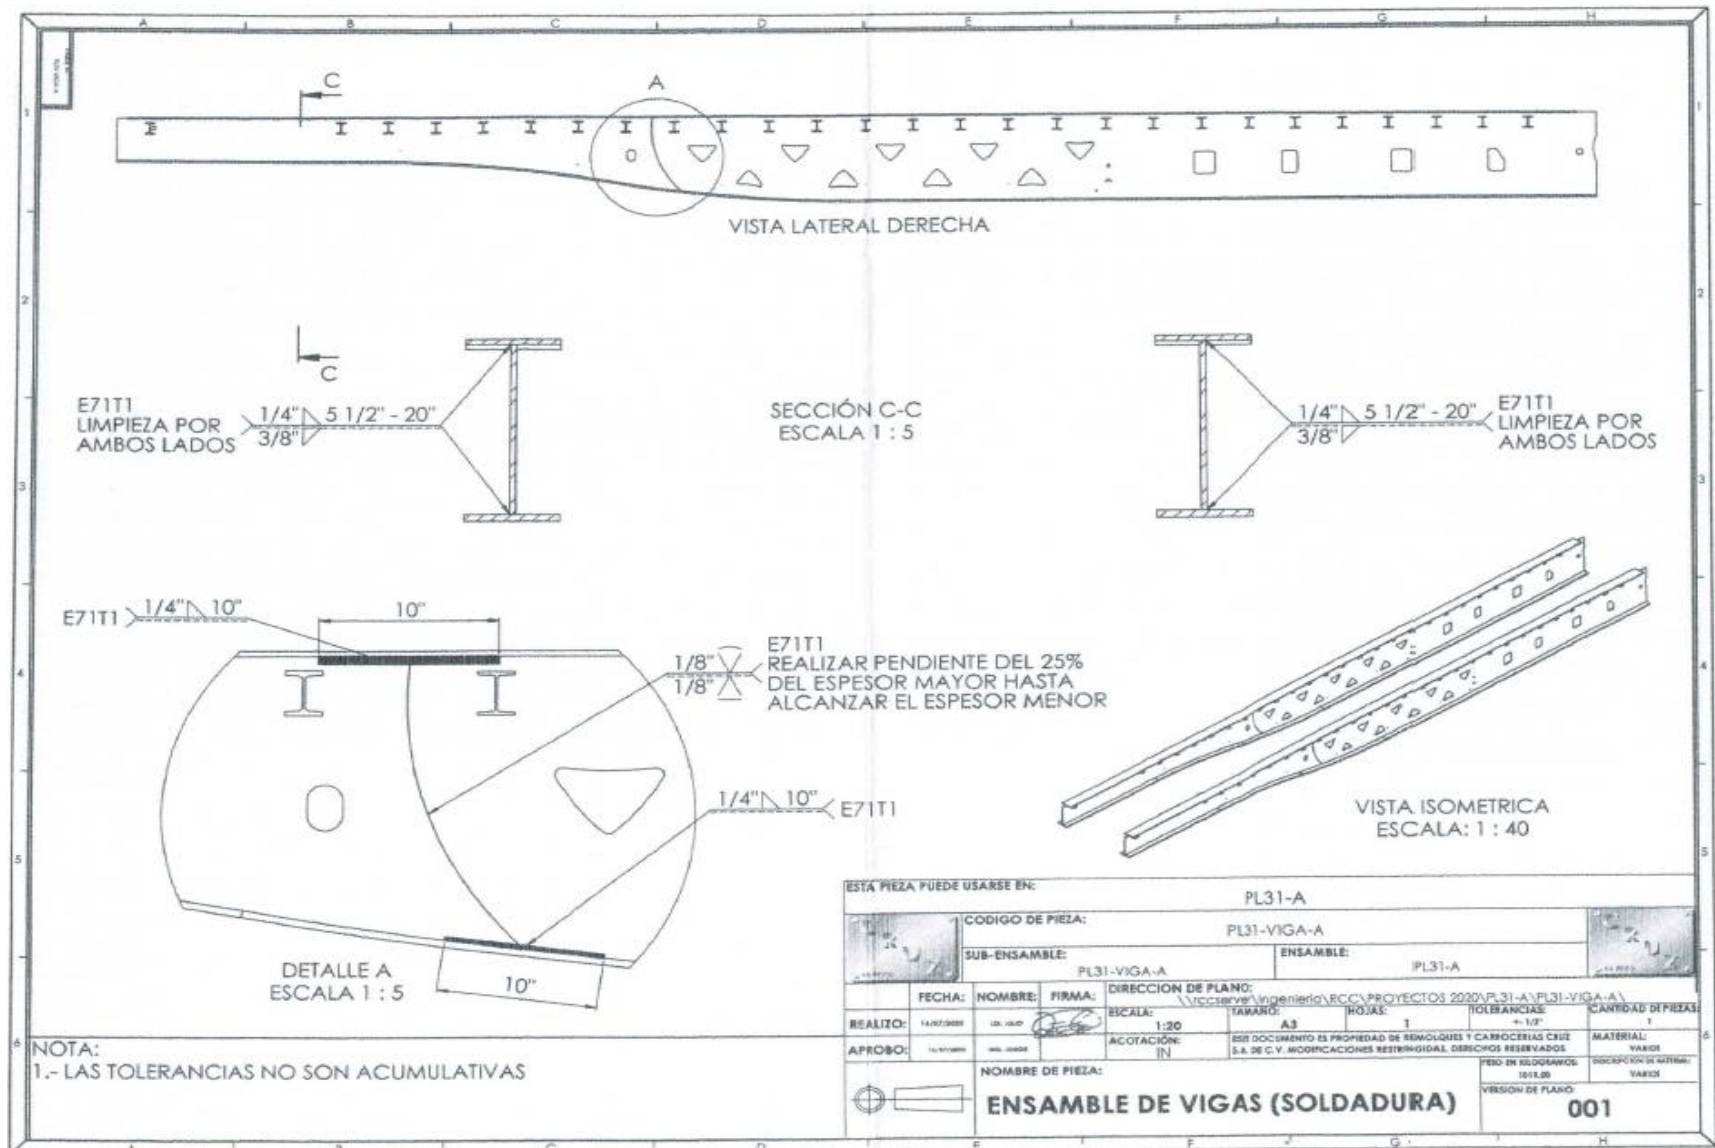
Plano del ensamble de vigas (soldadura). Fuente: Remolques y Carrocerías Cruz, S.A. de C.V., 2020.
